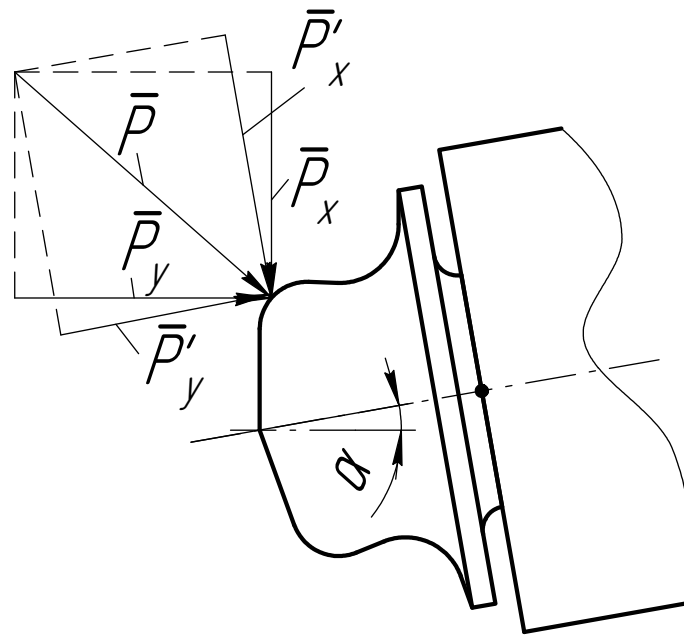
Розкладання повного зусилля, що діє на валок вздовж осі обертання валка та вдовж осі обертання заготовки
